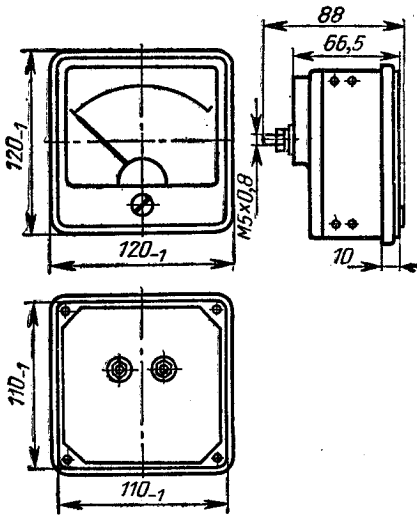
Габаритный чертеж прибора типа Ц330.
